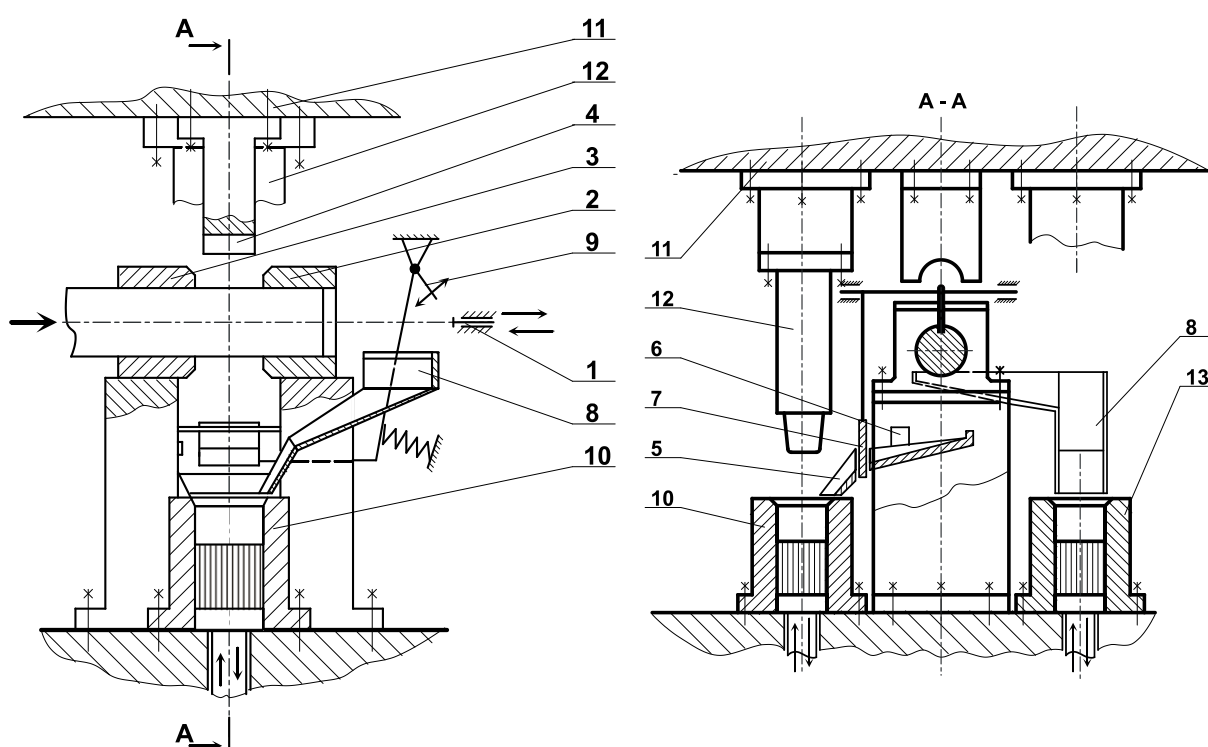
Штамп для комплексного заготовительно-разделительного процесса [145]
